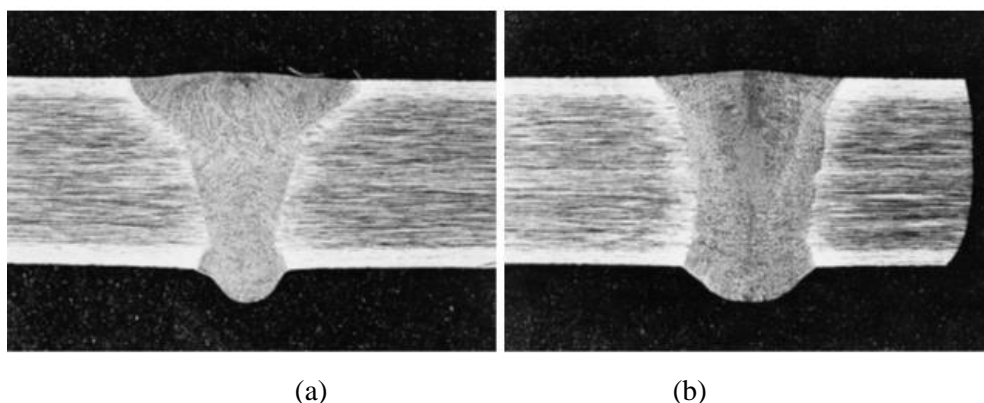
Sessões da soldagem (a) PAW e (b) A-PAW com as mesmas condições de soldagem: Aço inoxidável AISI 316L de 6mm de espessura soldado com energia de soldagem de 1,34 KJ/mm.
